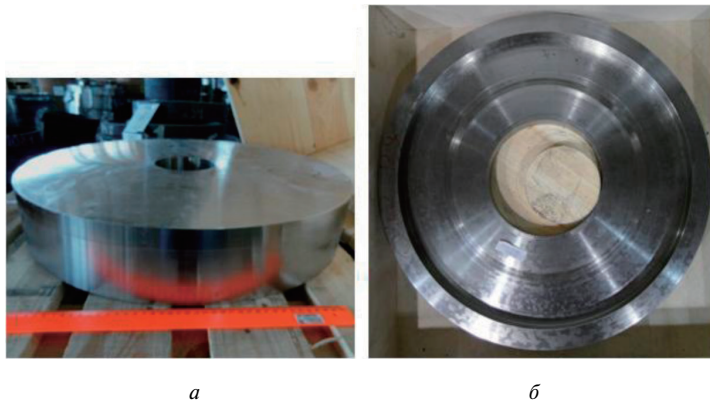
Внешний вид полученной заготовки из сплава ВЖ172-ИШ (а) и её внешний вид после черновой механической обработки (б)
